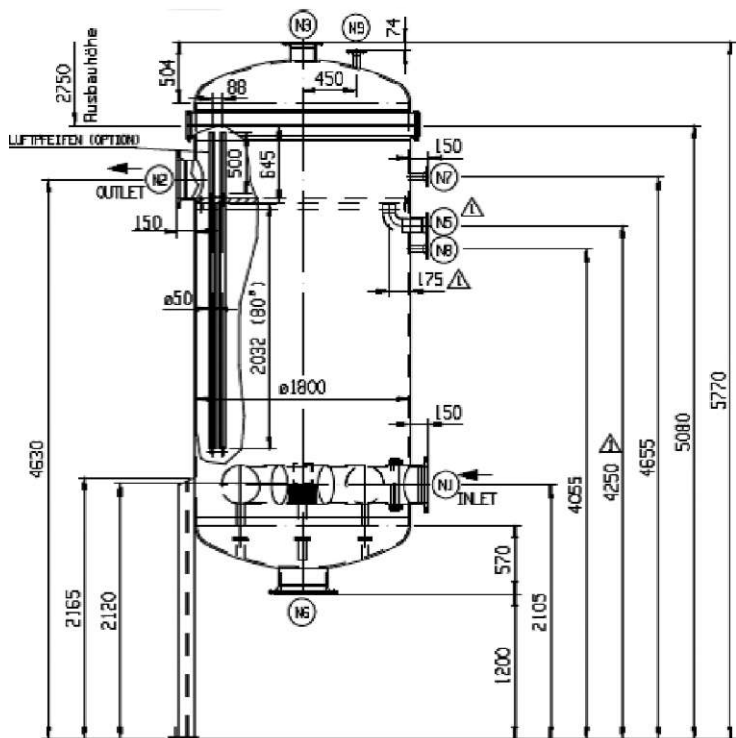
Схема конструкции и внешний вид патронных фильтров на Калининской АЭС
